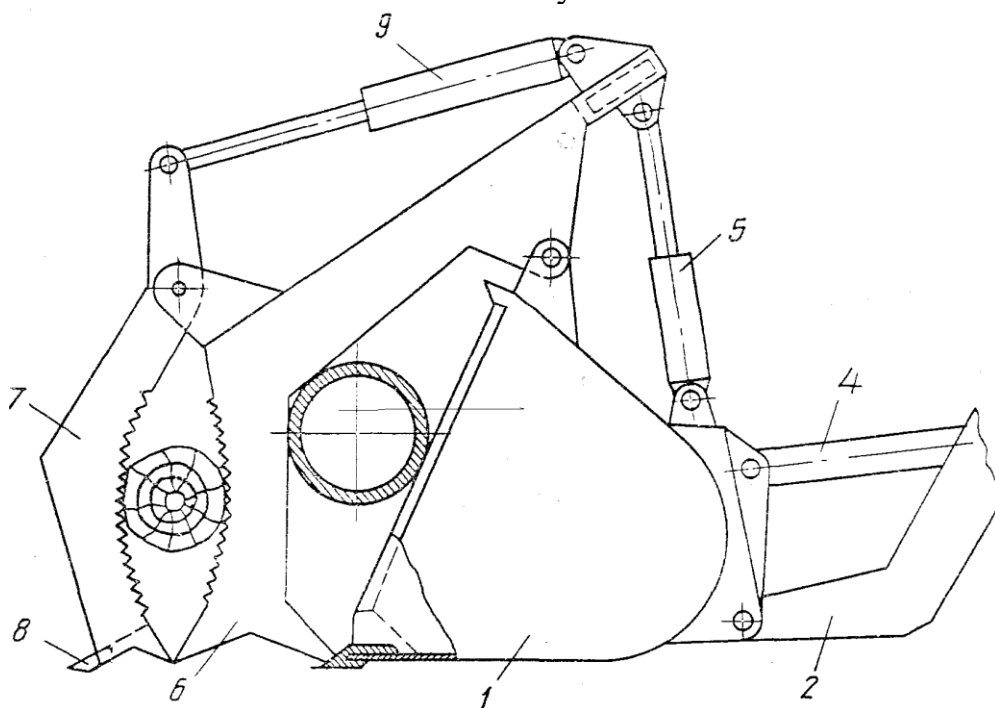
Конструктивна схема навісної щелепи універсального будівельного навантажувача
